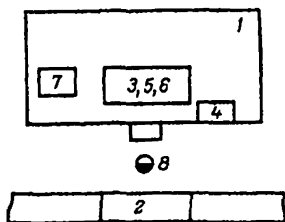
Схема планировки рабочего места шлифовщика: 1 — шлифовальный станок; 2 — конвейер для подвешивания деталей; 3 — зона установки и снятия детали; 4 — зона управления станком; 5 — зона технологического воздействия; 6 — зона контрольных измерений; 7 — зона хранения контрольно-измерительного инструмента; 8 — рабочее место шлифовщика
